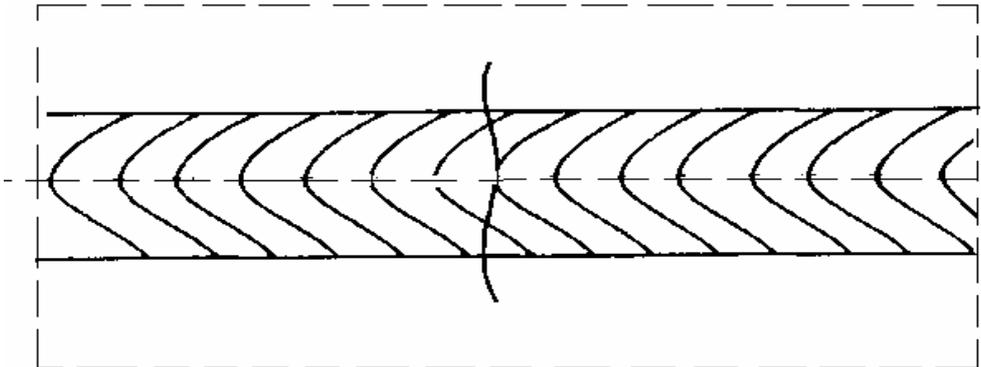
Поперечная трещина сварного соединения
